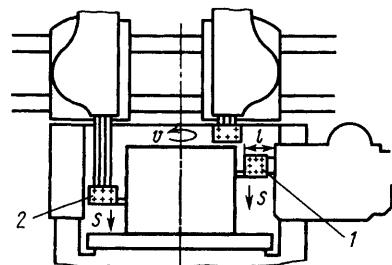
Схемы обтачивания наружной цилиндрической поверхности резцами вертикального и бокового суппортов
